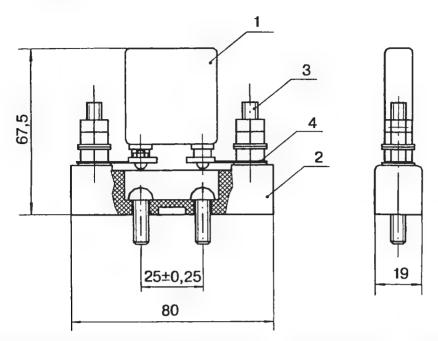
Внешний вид блока БЗП 1-10, где: 1- варистор; 2- контактная колодка; 3- болт; 4- контакт
